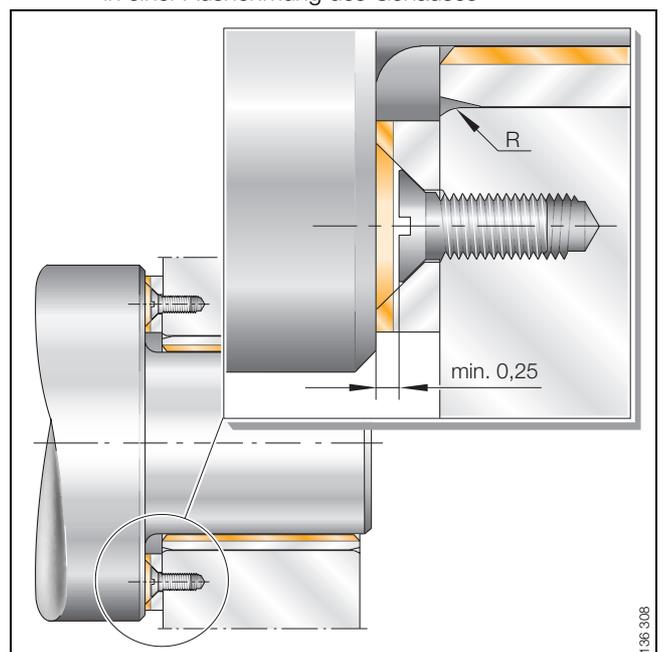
· Befestigen einer Anlaufscheibe PAW ohne Ausnehmung im Gehäuse
